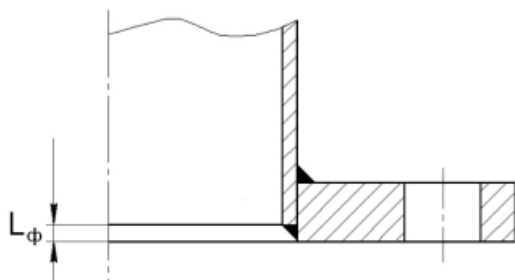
Толщина ответного фланца за вычетом длины посадки на трубопровод
